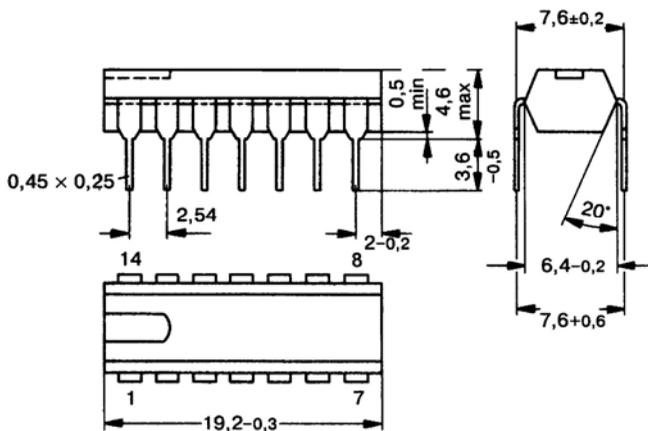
Корпус DIP с двухсторонним расположением выводов
